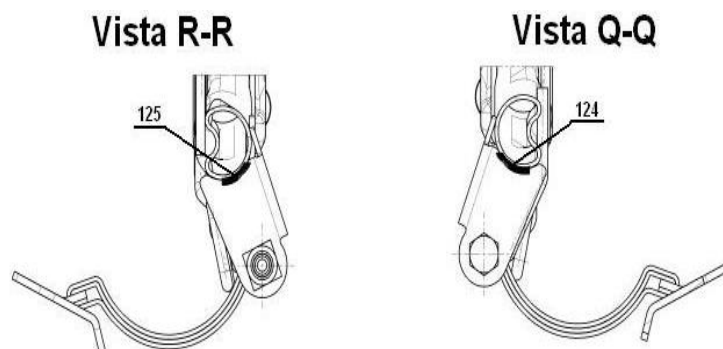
Localização dos cordões de soldadura - Cortes R-R e Q-Q
